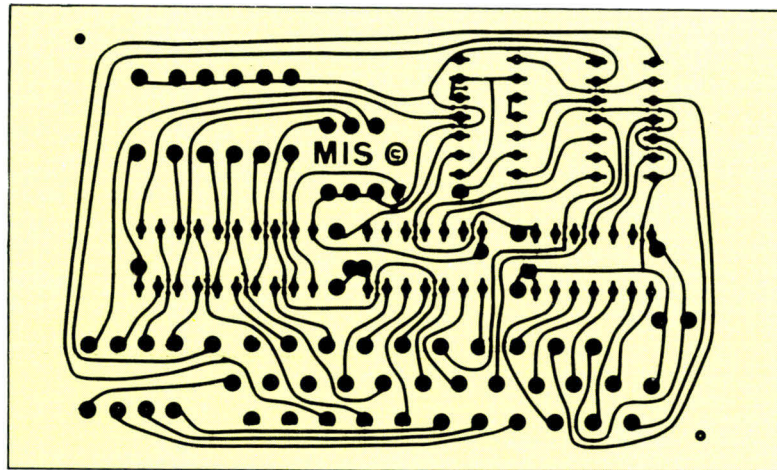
Circuit imprimé vu côté « soudures » (Ech. 1).
